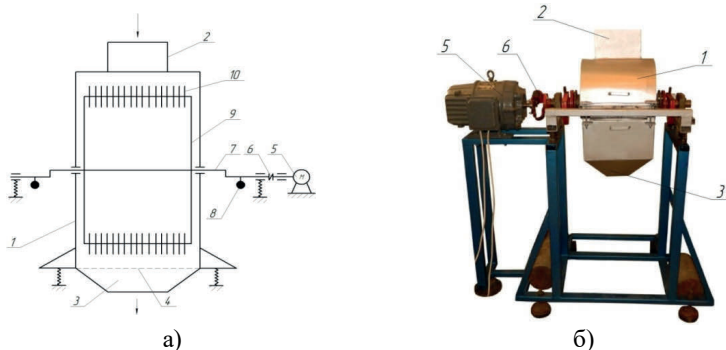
Вібраційна дискова дробарка: а) – принципова схема; б) – загальний вигляд; 1 – корпус; 2, 3 – завантажувальна та розвантажувальна горловина; 4 – сито; 5 – електродвигун; 6 – муфта еластична; 7 – вал кінематичний; 8 – противаги; 9 – ротор; 10 – біла дискового-типу.
